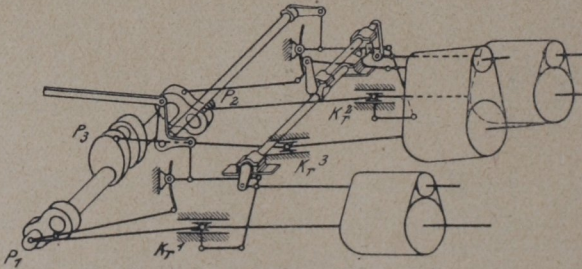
Steuerung der Drillinglokomotive Gattung G_{12} .
